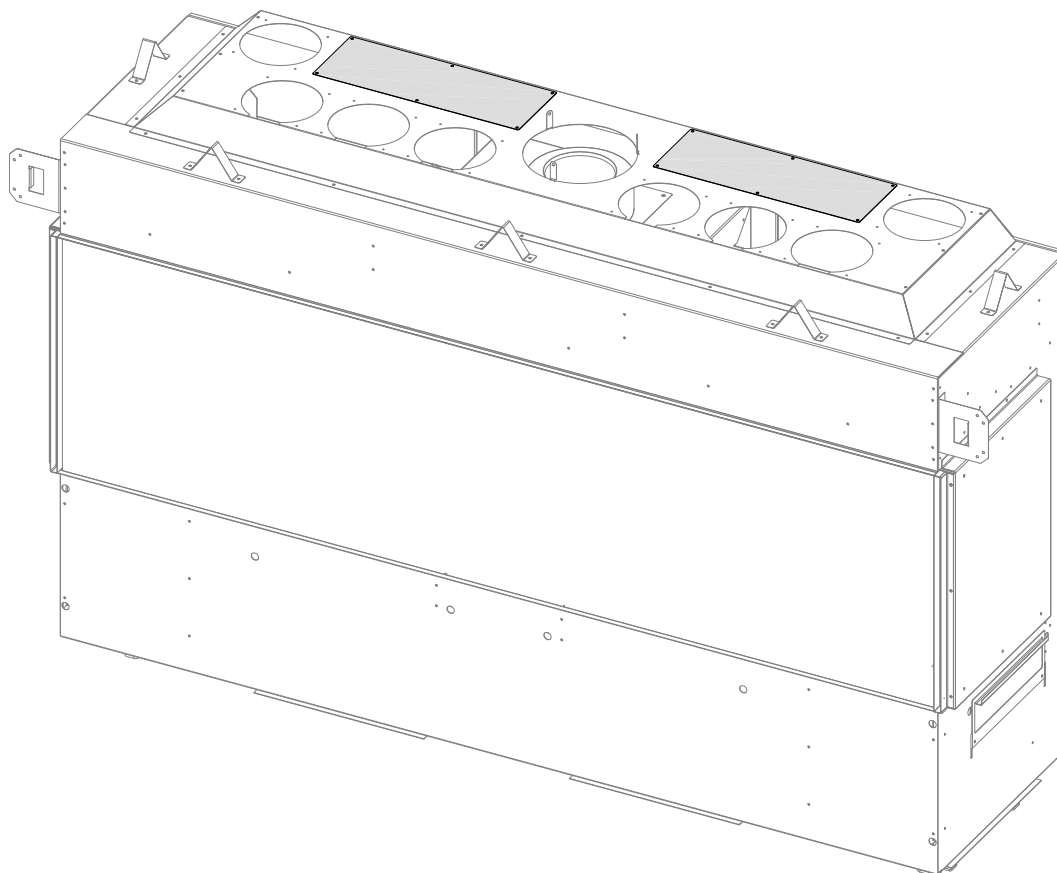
Emplacement des couvercles requis pour la cavité ventilée
